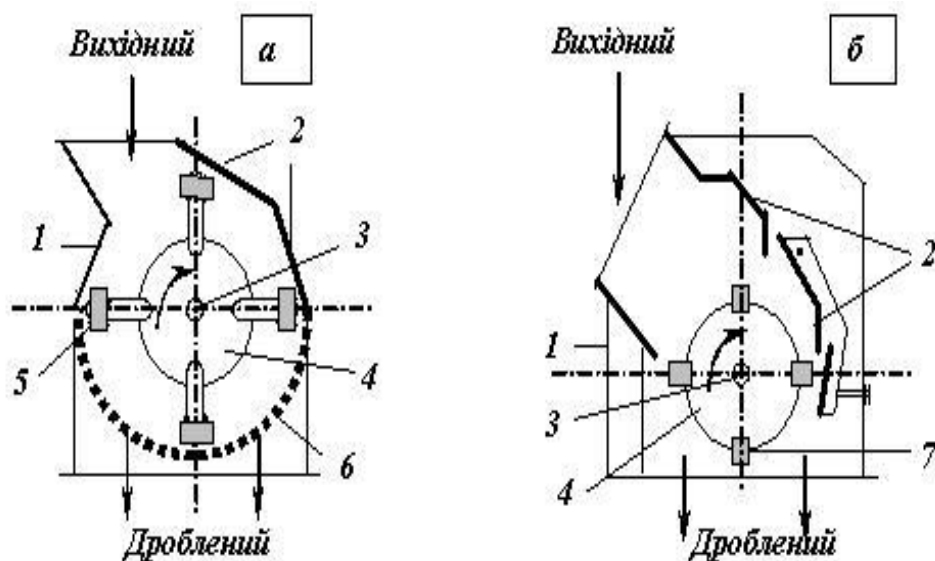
Дробарки ударної дії: а — молоткова дробарка; б — роторна дробарка; 1 — корпус; 2 — броньові відбійні плити; 3 — вал; 4 — ротор; 5 — молотки; 6 — колосникова решітка; 7 — било
